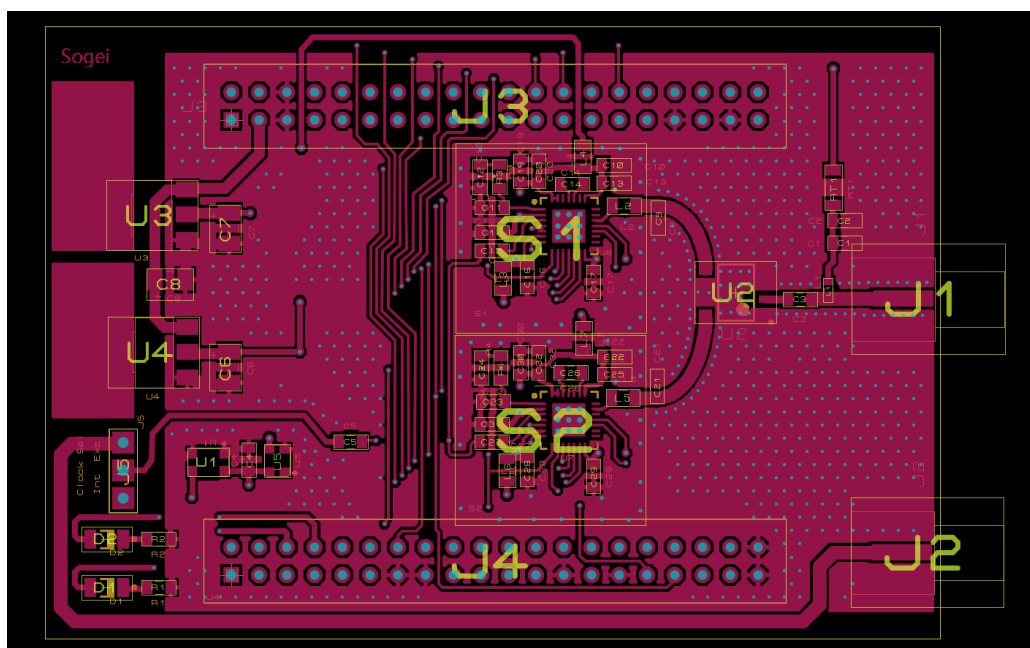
Bottom View del circuito da realizzare (componente A1)
